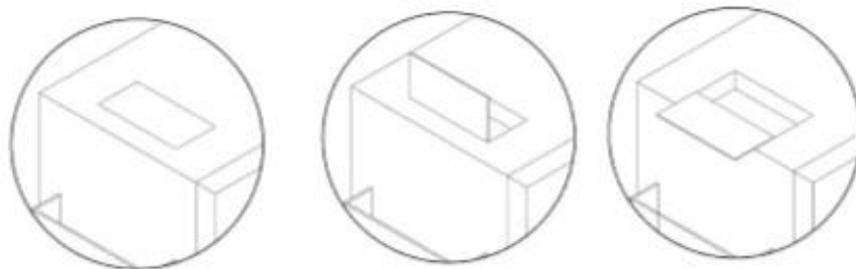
Pormenor da abertura tipo Tip-On do rebaixo existente na mesa. (Fonte: AutoCAD)
